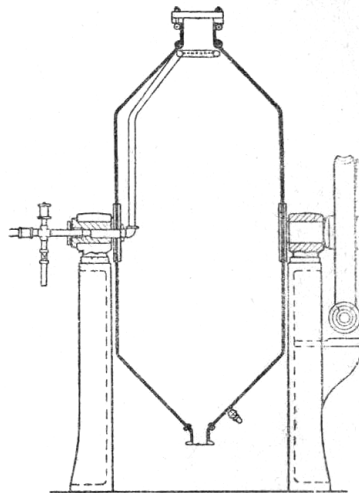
Вращающийся штуцерный котел для натронной варки древесины
